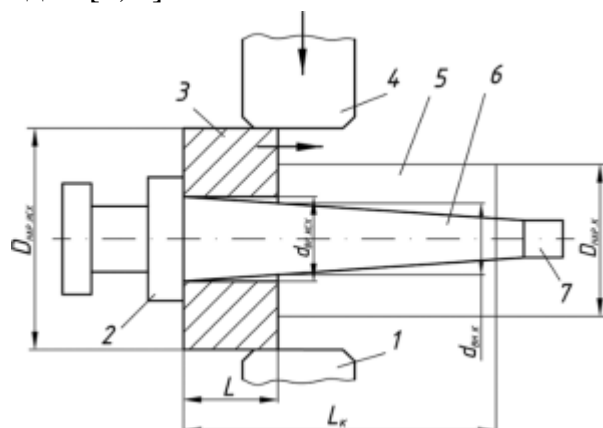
Схема протяжки полой заготовки: 1 – нижний вырезной боек; 2 – бурт оправки; 3 – заготовка; 4 – плоский боек; 5 – готовая поковка; 6 – оправка; 7 – отверстие для охлаждения водой
